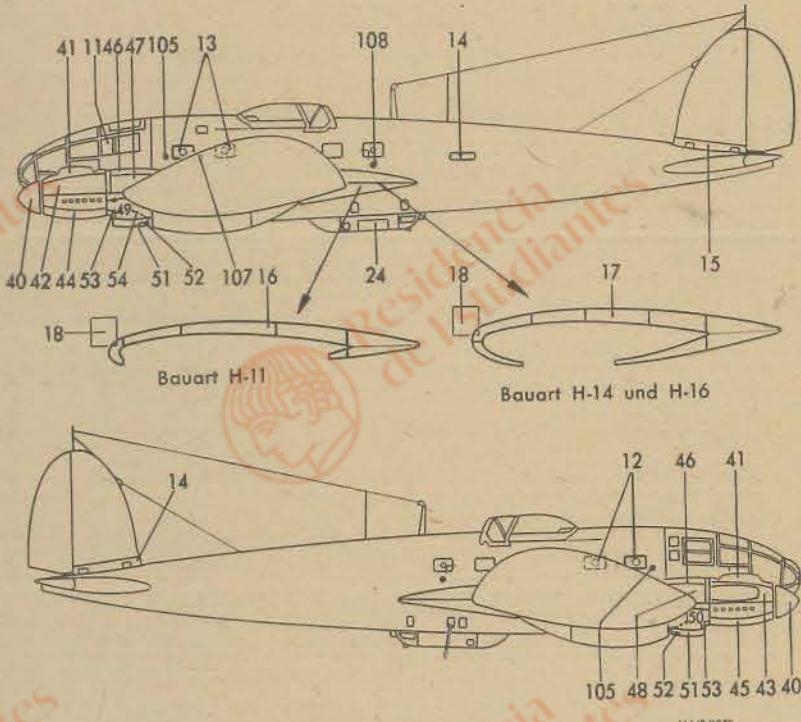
Deckel- und Klappenplan (Seitenansicht)
